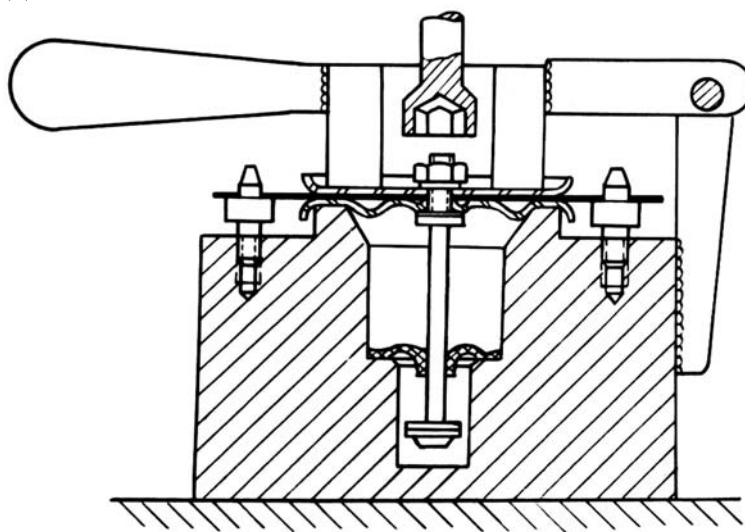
Приспособление для сборки диафрагмы топливного насоса
